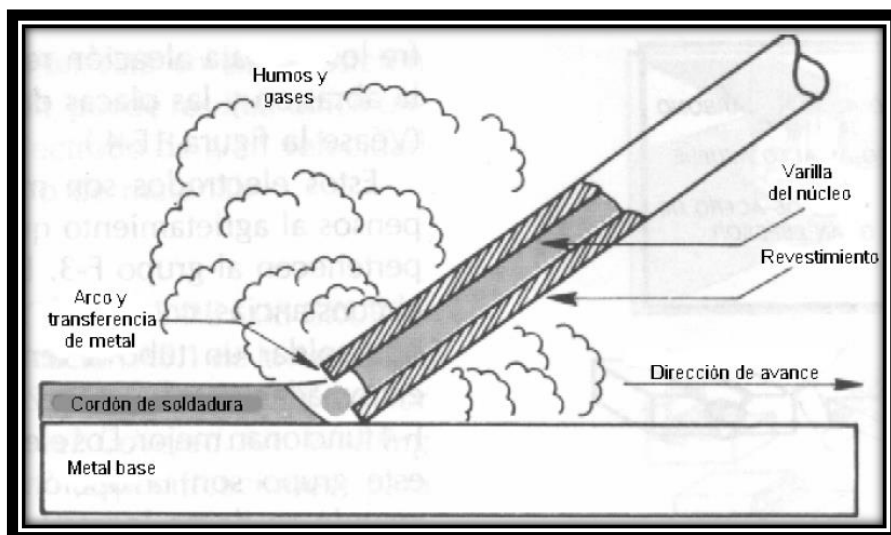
Tipo de soldadura para Bridas
